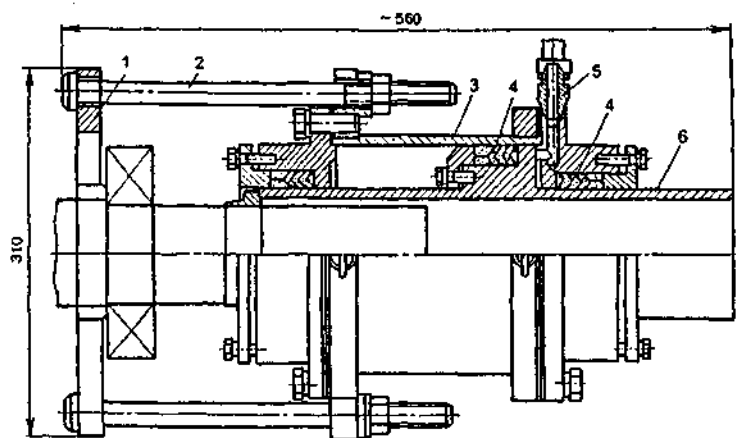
Гидравлический подвесной съемник для снятия подшипников с валов электродвигателей 6-9-го габаритов:
